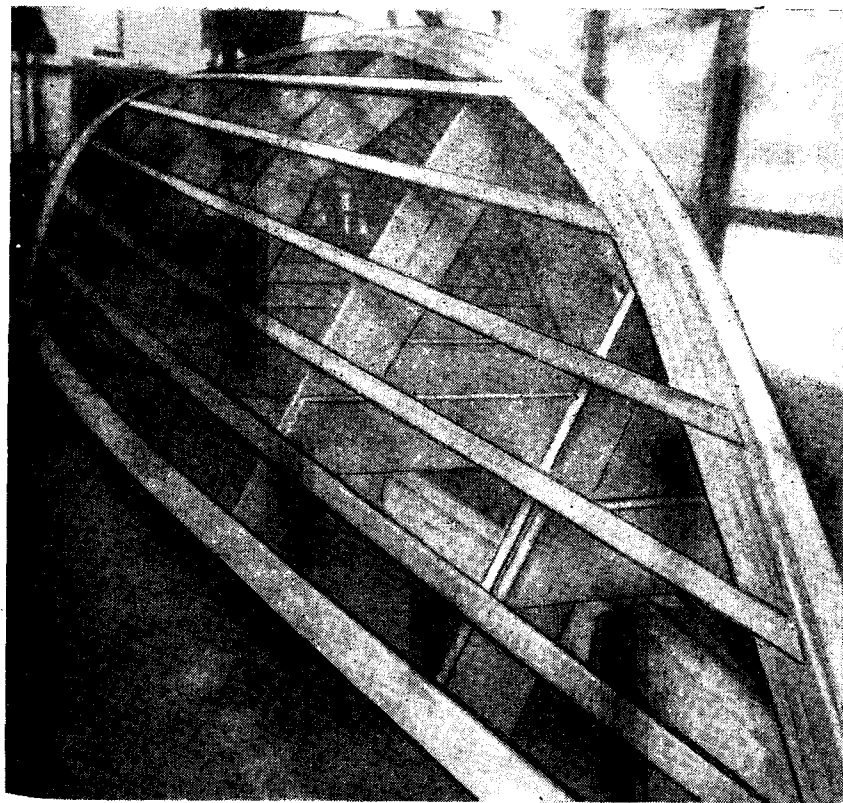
Стапель-кондуктор для постройки корпуса с диагональной обшивкой.
